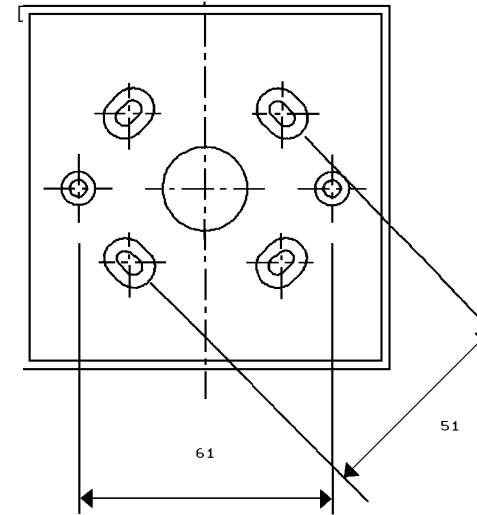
FC420CP-I Dimensioni di fissaggio della retroscatola per il montaggio a parete
